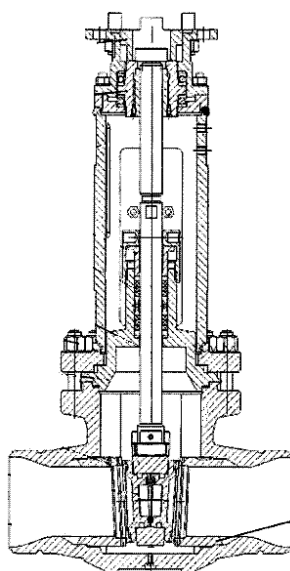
Общий вид задвижки клиновой сварной конструкции И. Р. Шегельмана, Г. Н. Колесникова и Е. А. Тихонова [16]
